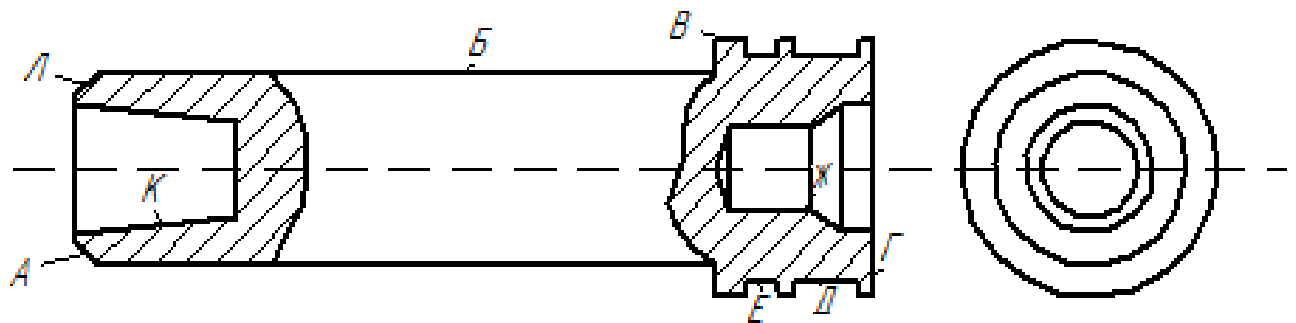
Ескіз штоку з позначеними оброблюваними поверхнями
